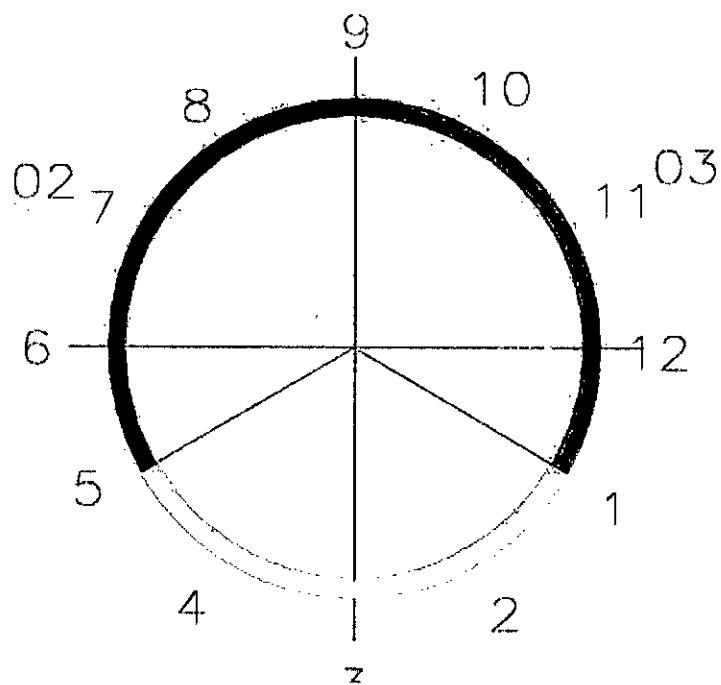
POSICIONES SOLDEO EXTERIOR
